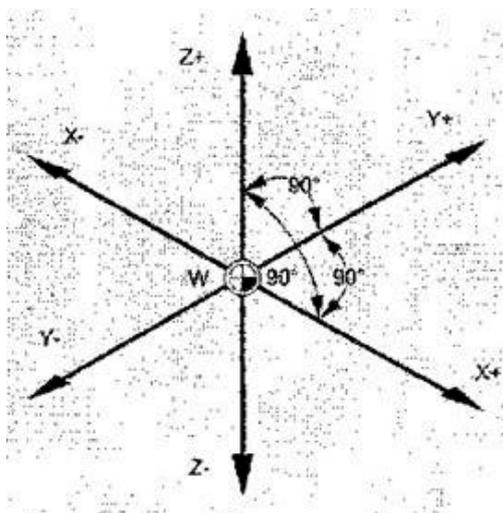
Направление осей X, Y и Z системы координат фрезерного обрабатывающего центра с ЧПУ
